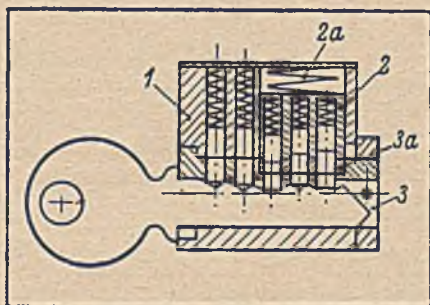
Schließzylinder mit geteiltem Innenzylinder
